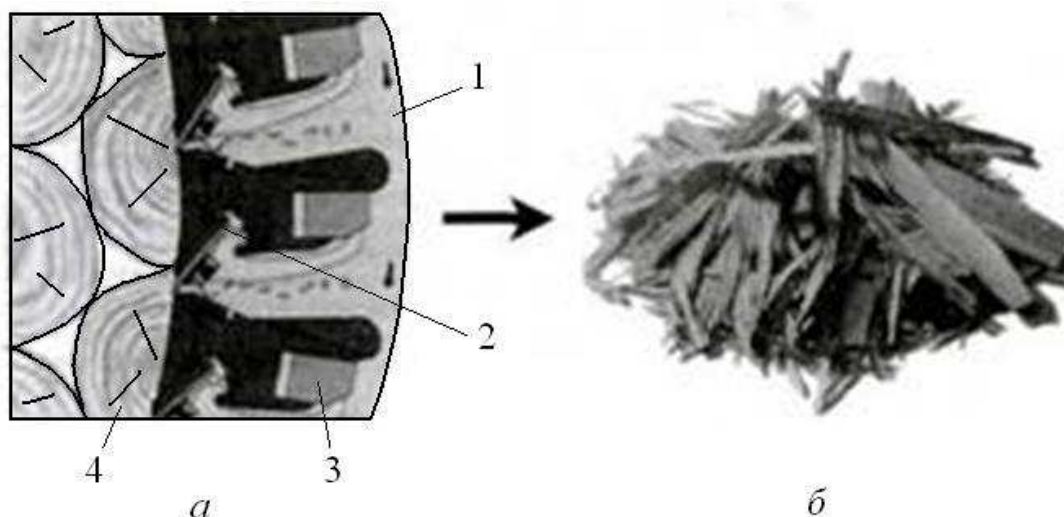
Срезание стружки при поперечном цилиндрическом фрезеровании древесины:
